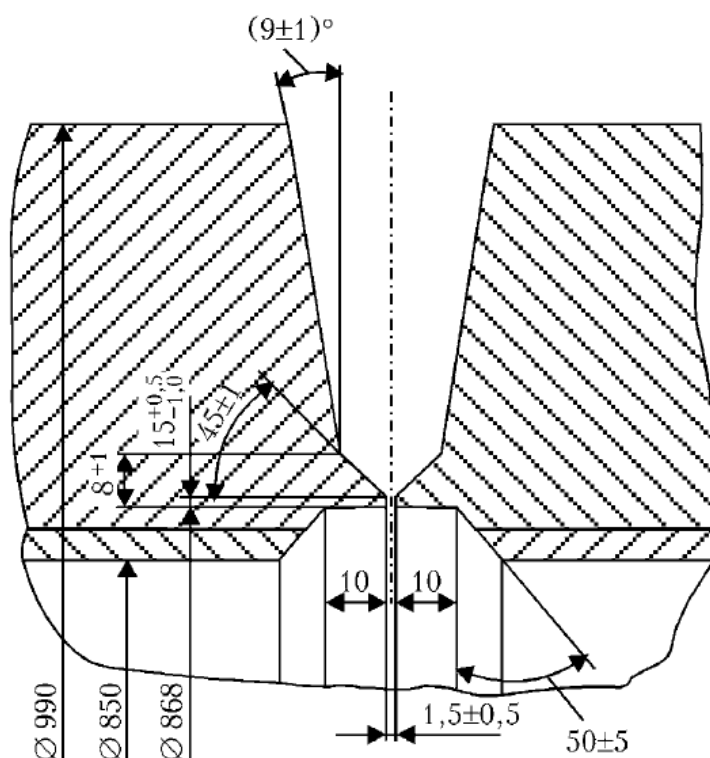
Форма стандартной разделки под выполнение автоматической аргодуговой сварки неплавящимся электродом
